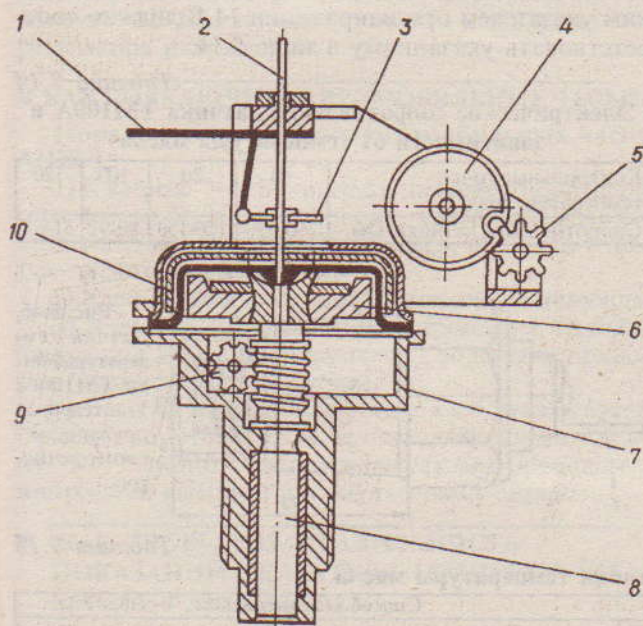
Механизм спидометра: 1 - пластина регулировочная; 2 - ось стрелки; 3 - волосок; 4 - барабанчик счетного узла; 5 - трубки; 6 - магнит; 7 - корпус; 8 - валик привода спидометра ведущий; 9 - валик ведомый; 10 - катушка
